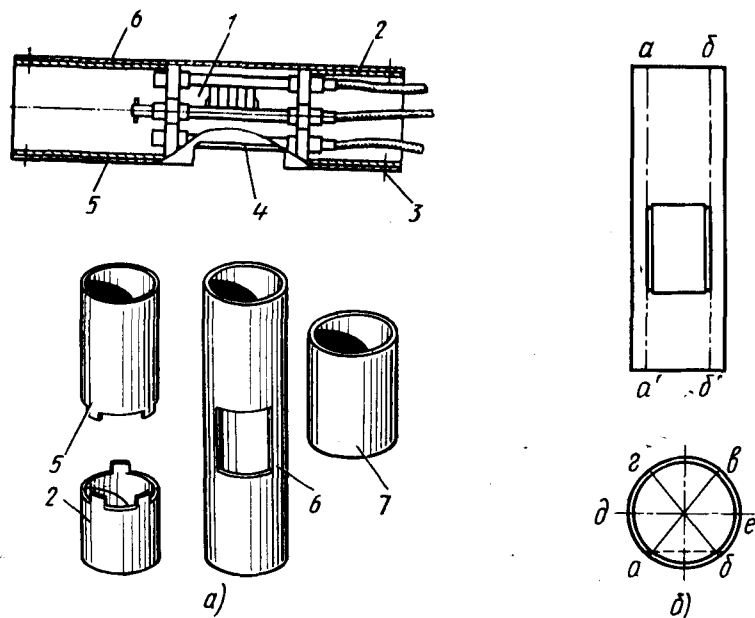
Комплектовка переключателя бумажно-бакелитовыми цилиндрами (а) и разметка общего цилиндра (б):
